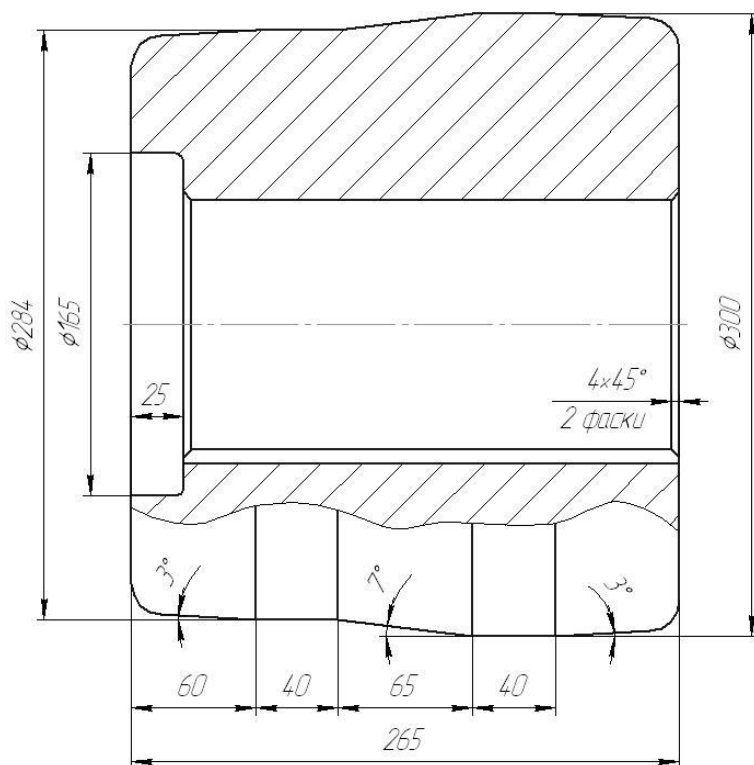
Калибровка валка лабораторного стана «УралНИТИ» для исследования процесса риллингования с уменьшением диаметра трубы
